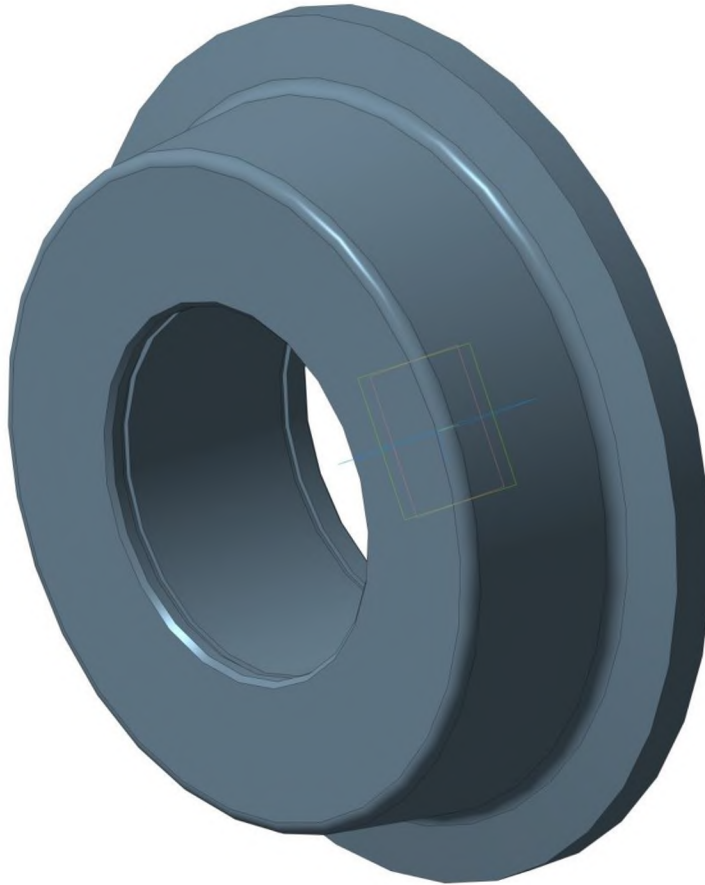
Креслення деталі «Ролик утримуючий»
